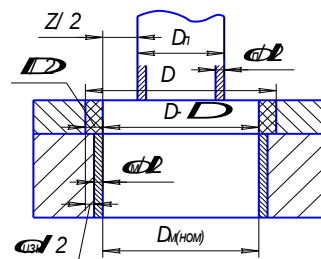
Схема расположения полей допусков на исполнительные размеры матрицы при вырубке отверстия в детали «пластина».
